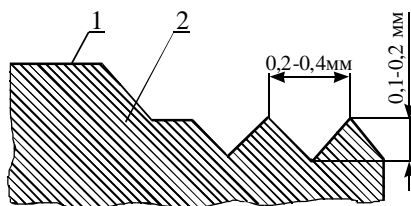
Підготовка поверхні методом нарізання „рваної” різби: 1 – зняття спрацьованого шару; 2 – підготовка поверхні зчеплення
